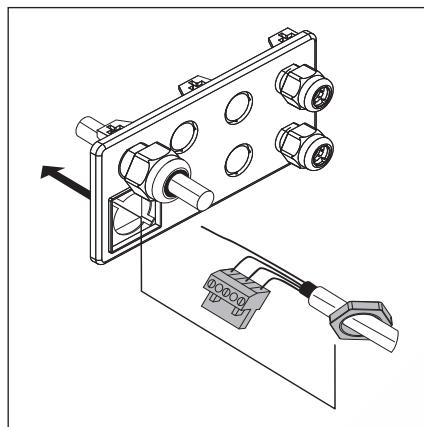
Stecker und Befestigungsmutter durch die Flanschplatte fädeln
